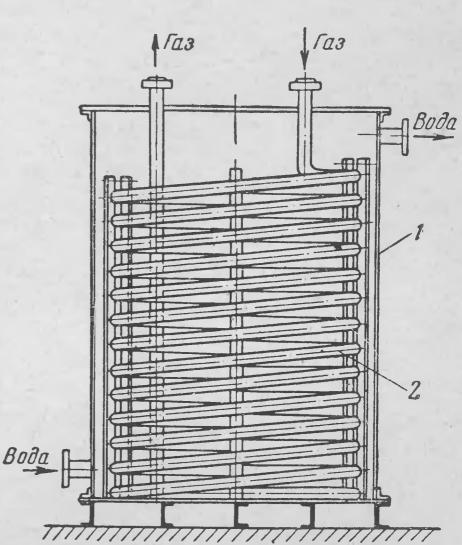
Холодильник змеевикового типа. 1 — резервуар (ванна); 2 — змеевик.
